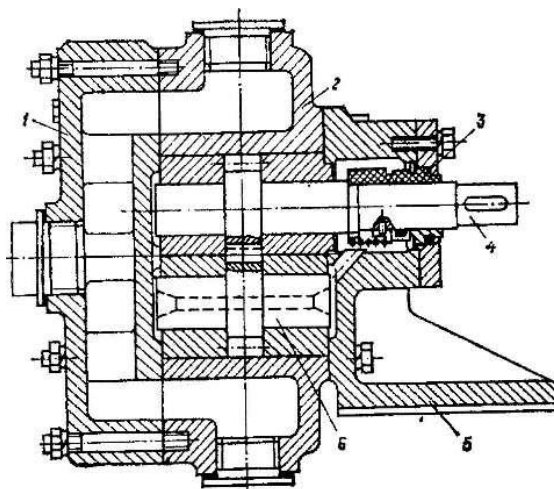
Шестеренчатый насос типа Ш: 1 - крышка обогревательного канала ; 2 - корпус; 3 – уплотнение, 4 - ведущий ротор; 5 - стойка; 6 - ведомый ротор
